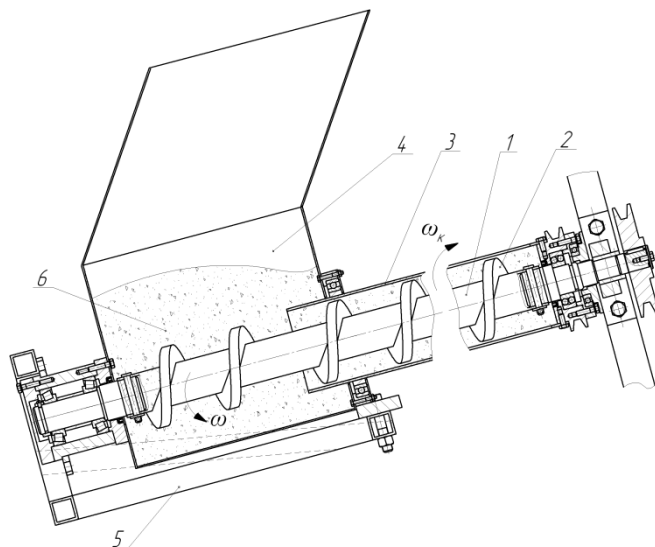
Конструкційна схема гвинтового конвеєра з обертовим кожухом: 1 – привідний вал; 2 – гвинтовий робочий орган; 3 – обертовий кожух; 4 – бункер; 5 – рама; 6 – матеріал, що переміщується
